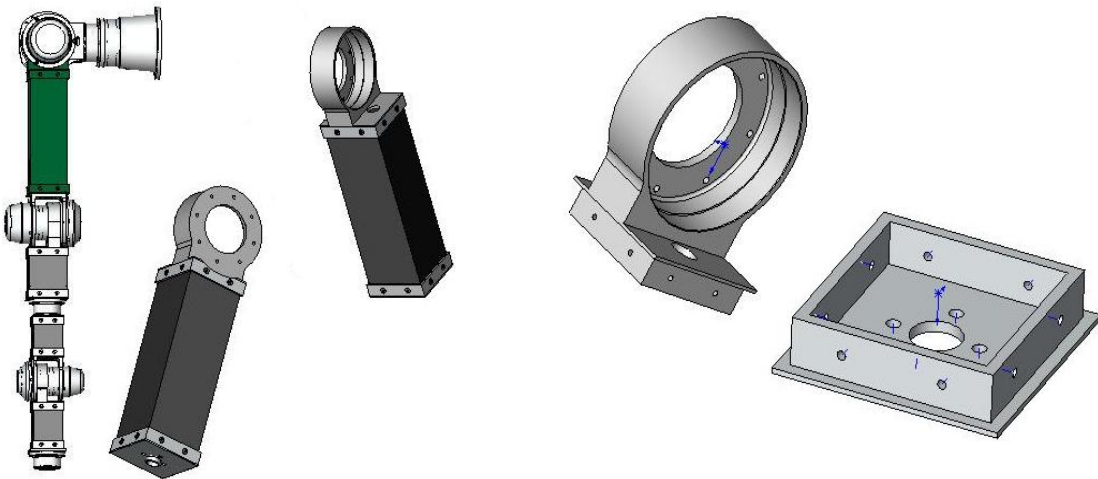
Vista sub-ensamblaje sección cuadrada y piezas de la misma sección.
